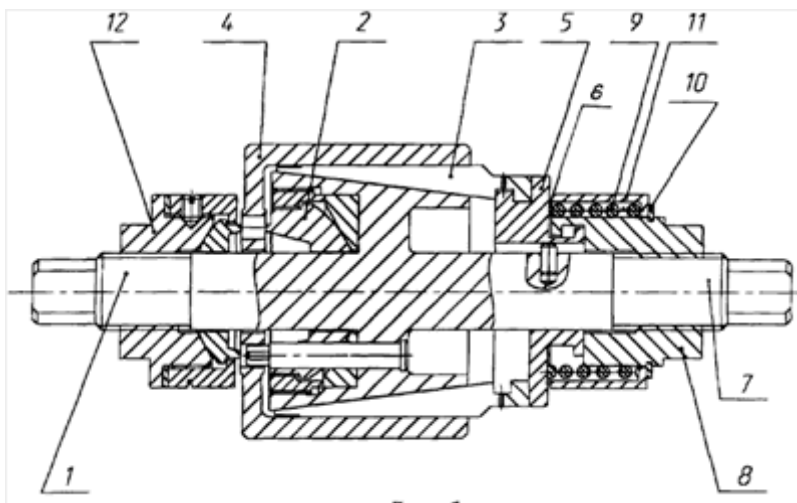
устройство для закрепления детали в положении черновой обработки заготовки по патенту РФ 2329124, общий вид в разрезе;
